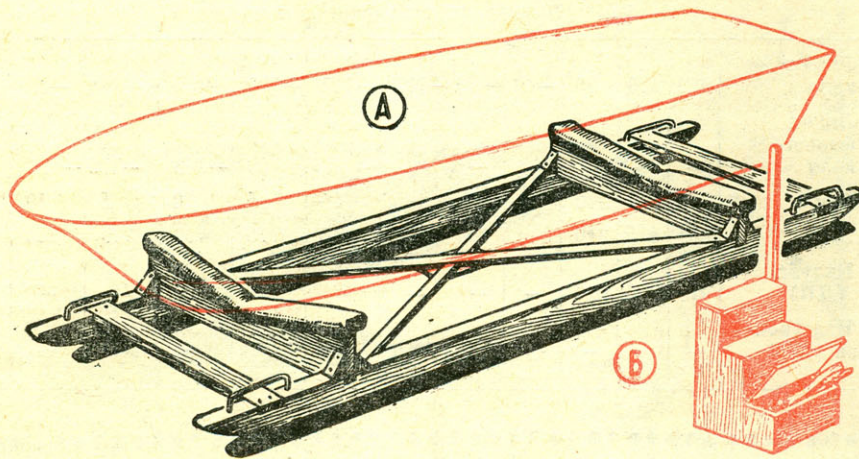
Установка корпуса для выполнения внутренних работ и окончательной отделки: А — корпус на кильблоках; Б — стремянка, служащая одновременно ящиком для инструментов и крепежа.
